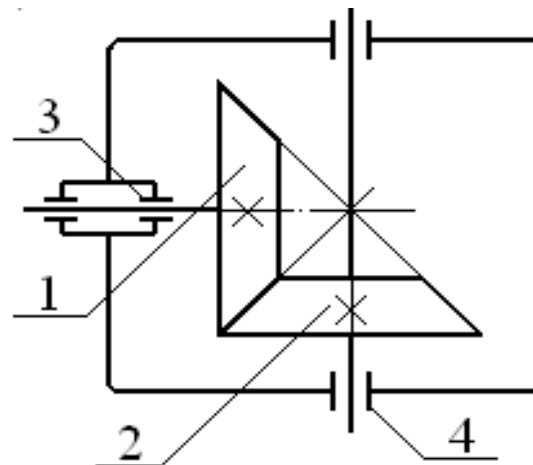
Схема редуктора конического одноступенчатого:
